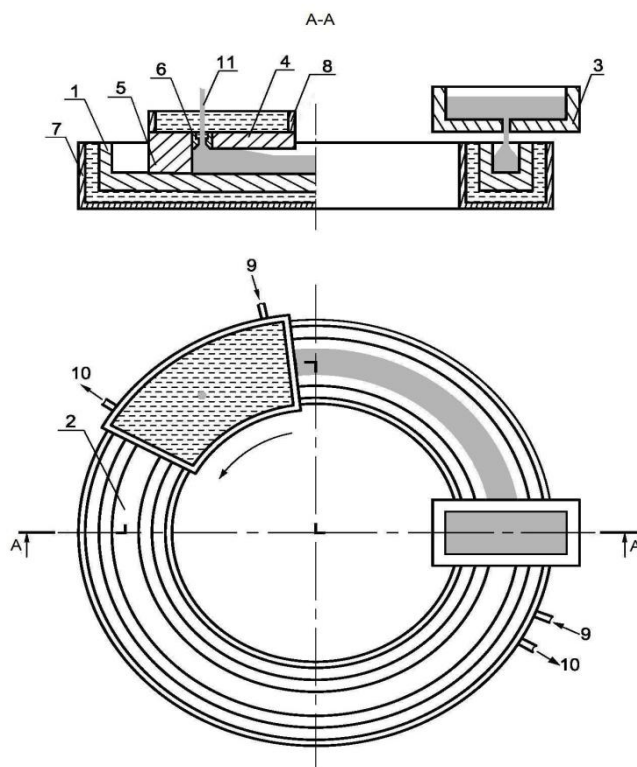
Устройство для охлаждения инструмента установки непрерывного литья-прессования цветных металлов и сплавов
